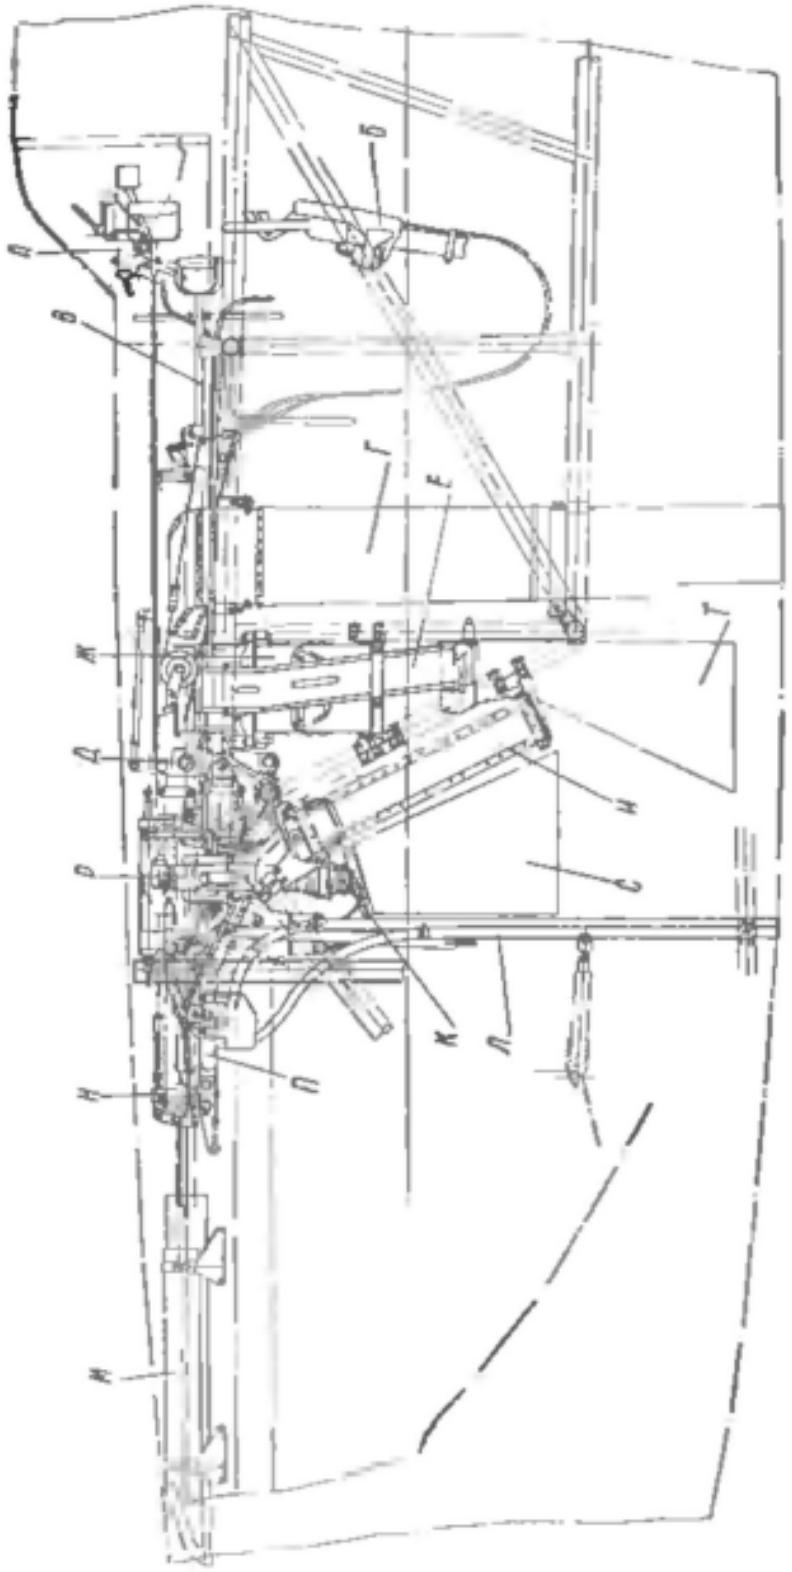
Общий вид стрелковой установки (вид сбоку).
